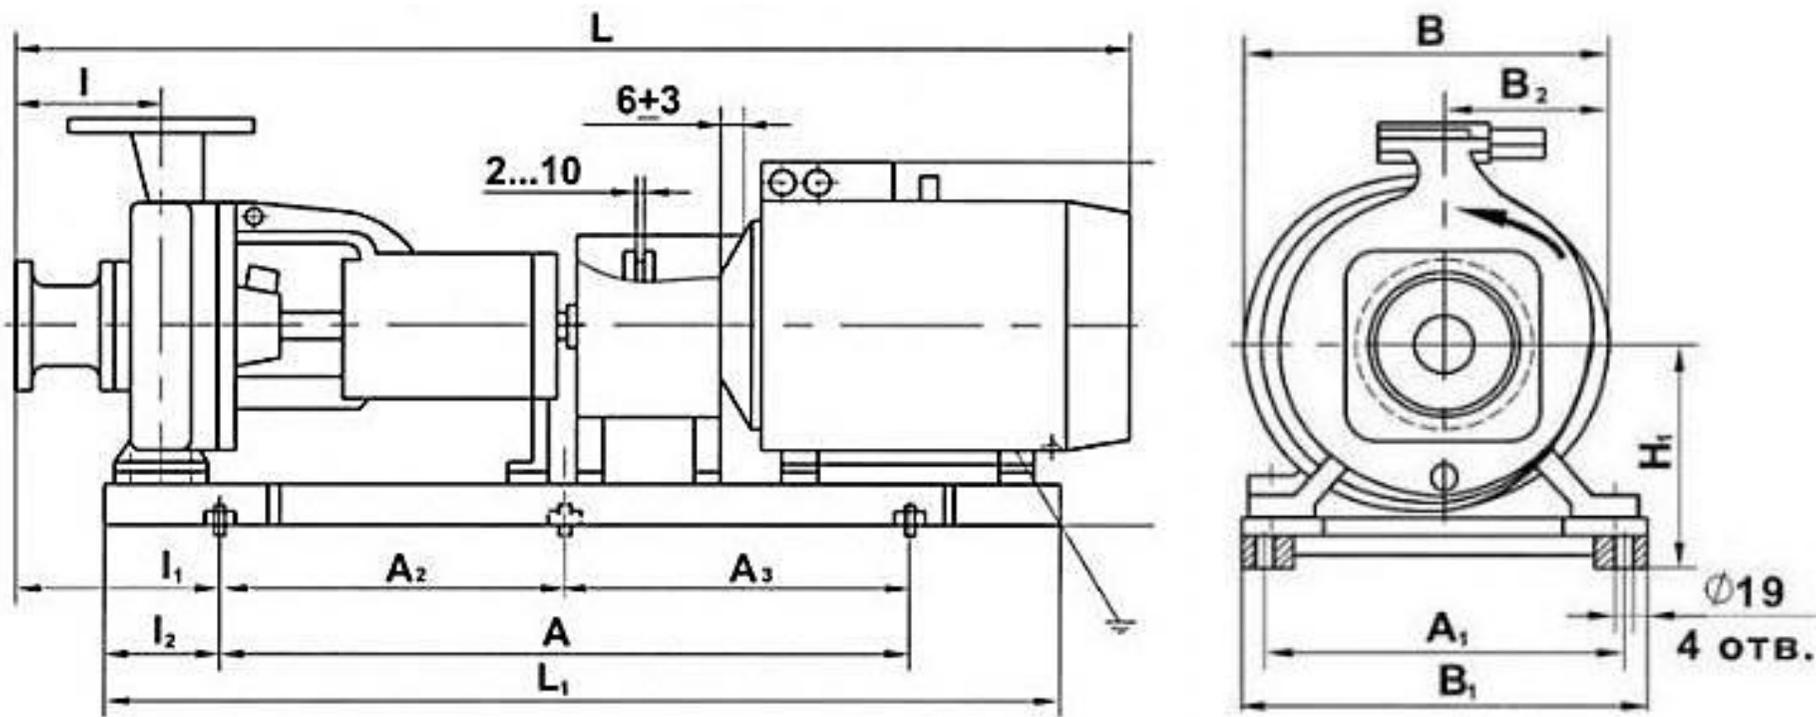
Габаритный чертеж насосного агрегата 1K100-65-250
